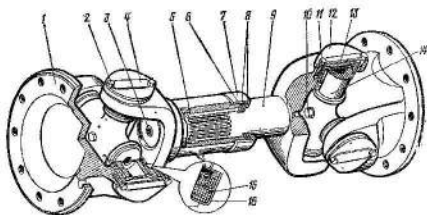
Карданный вал переднего ведущего моста: 1 — фланец вилки, 2 — болт, 3 — заглушка, 4 — стопорная планка, 5 — скользящая вилка, 6 — сальник, 7 — гайка, 8 — шайба, 9 — карданный вал, 10 — пробка, 11 — игольчатый подшипник, 12 — балансирующая пластина, 13 — крышка подшипника, 14 — крестовина, 15 — уплотнительное кольцо, 16 — обойма
